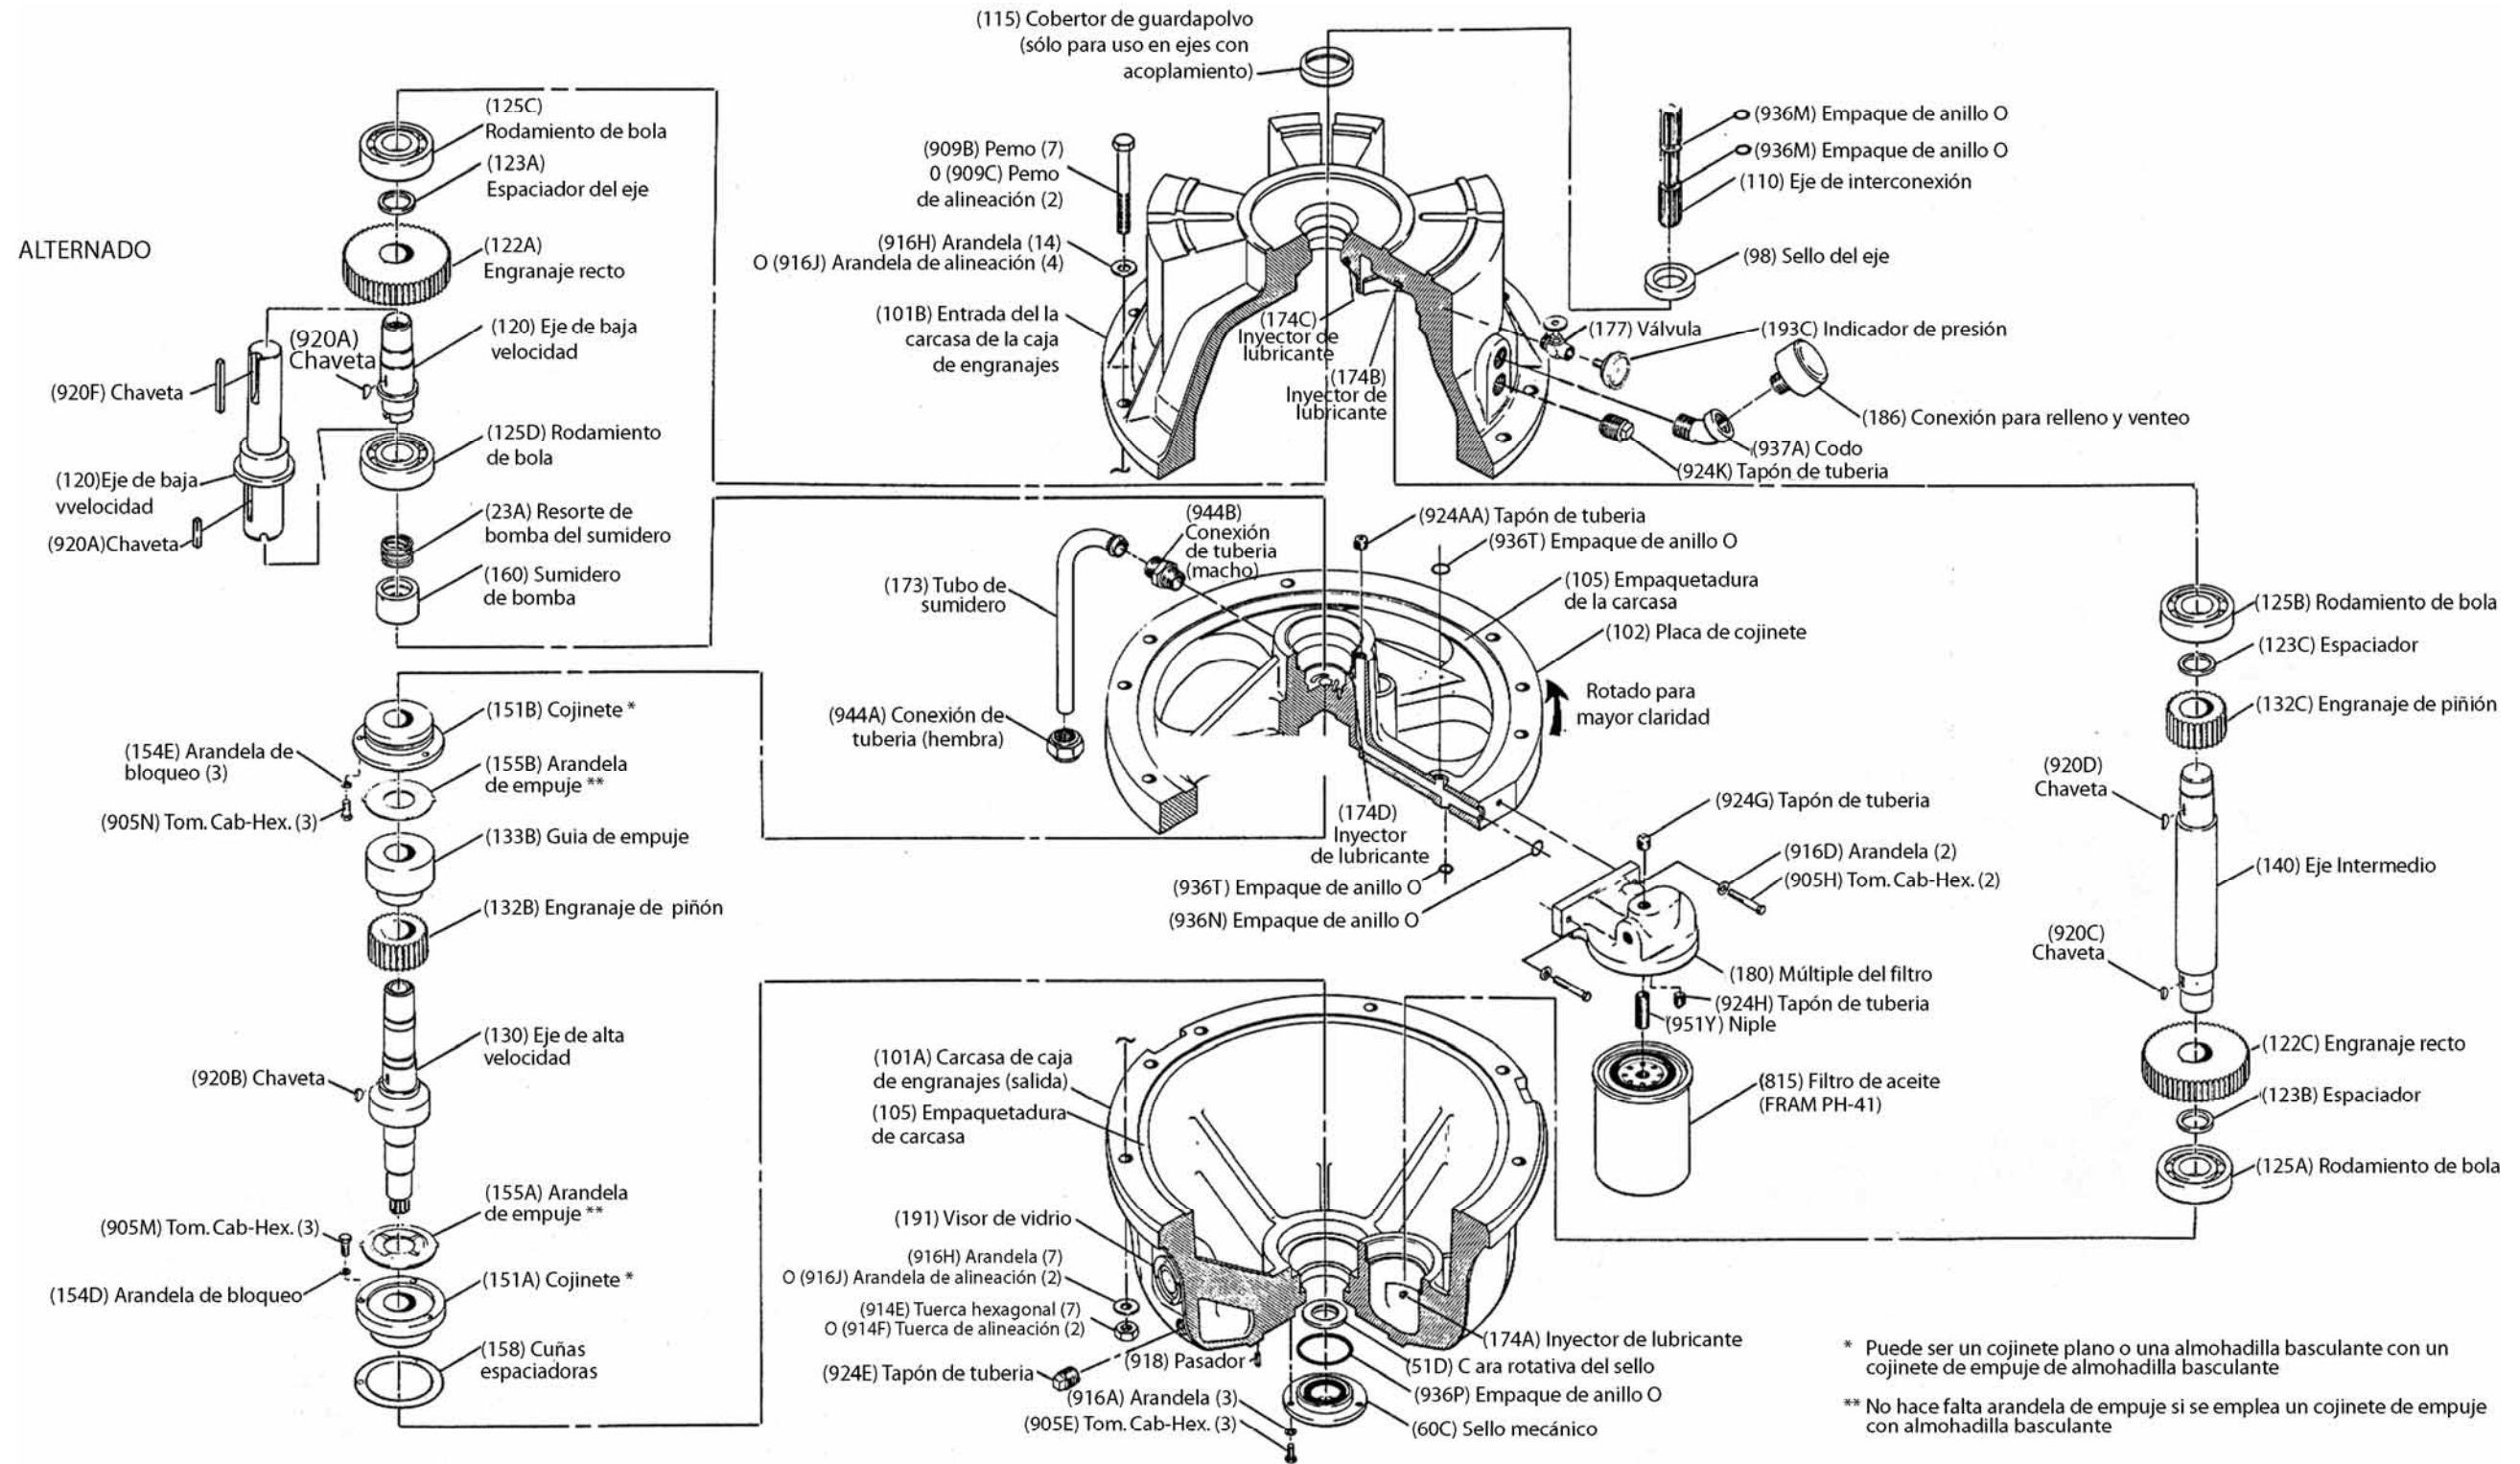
Sección transversal de la bomba y de la caja de engranajes
